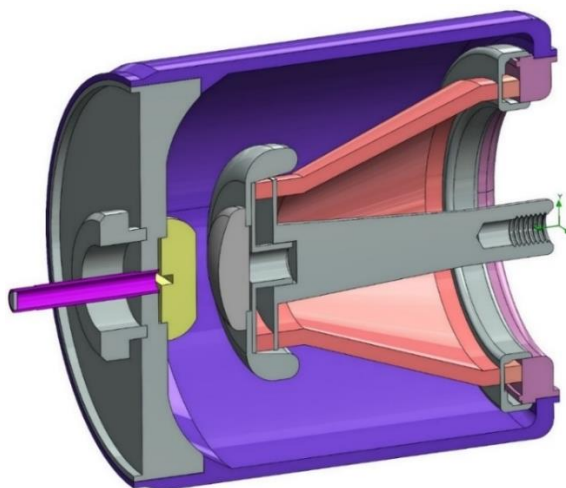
3D модель разрядника-обострителя РО-49 без резьбы
